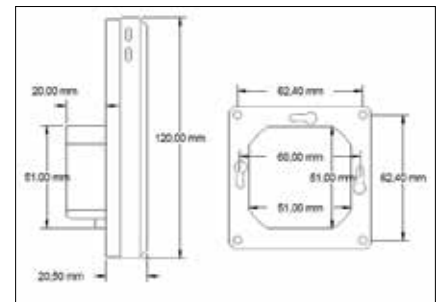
Croquis coté pour le montage dans un coffret mural ou un tableau mural
